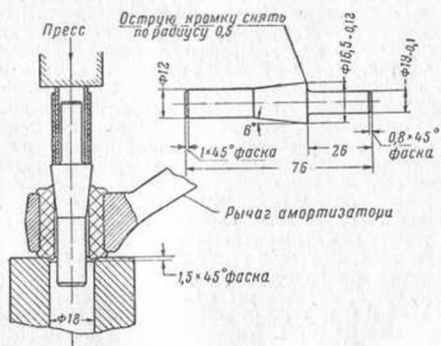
Приспособление и запрессовка бронзовой втулки амортизатора.
